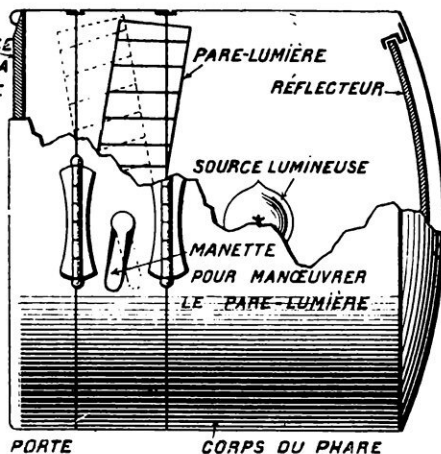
DISPOSITIF GÉNÉRAL DU PARE-LUMIÈRE A CADRE
